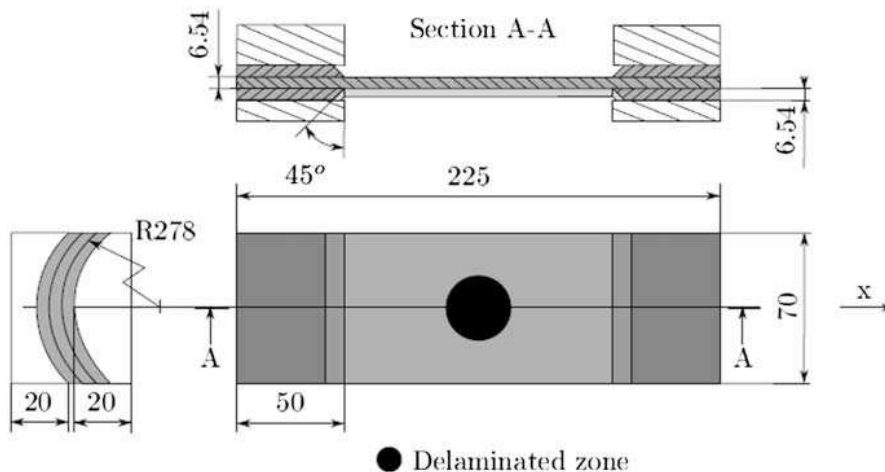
Géométrie des éprouvettes de traction (dimension en mm) L.Ballère [15]
